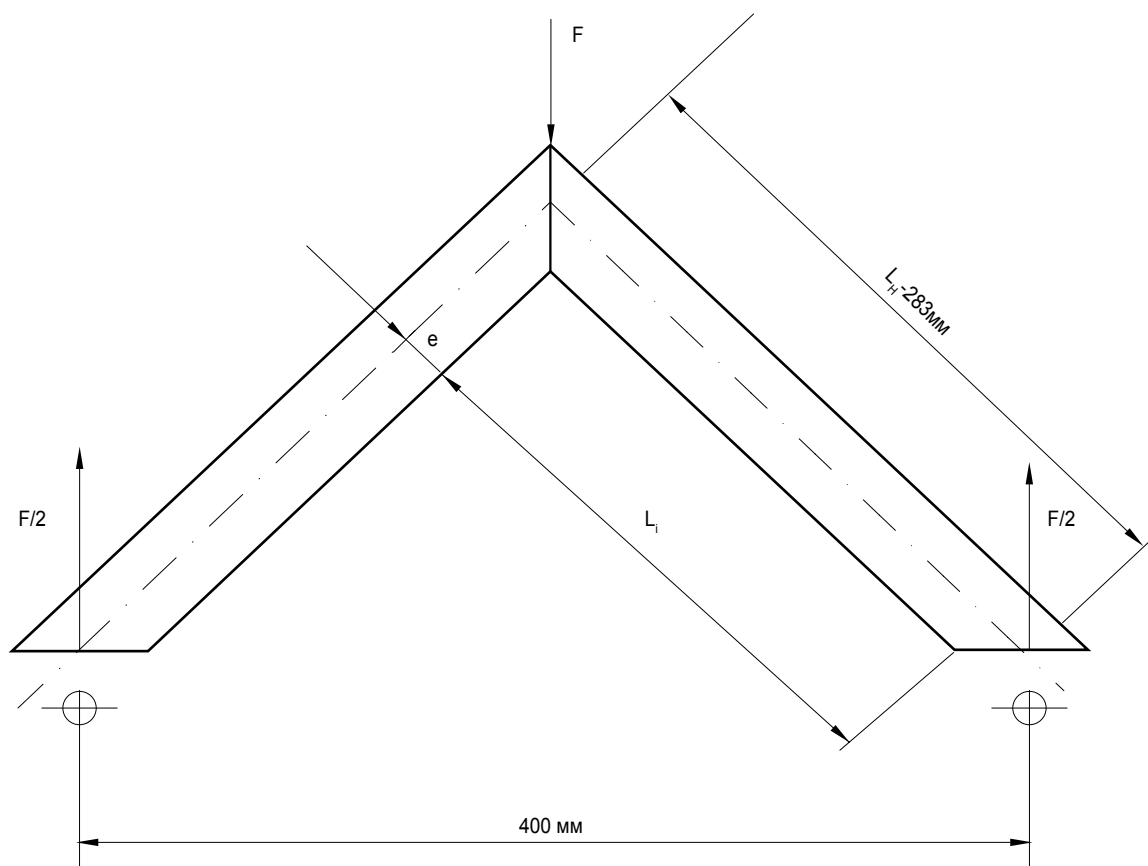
Эскиз образца для испытания углового сварочного соединения
